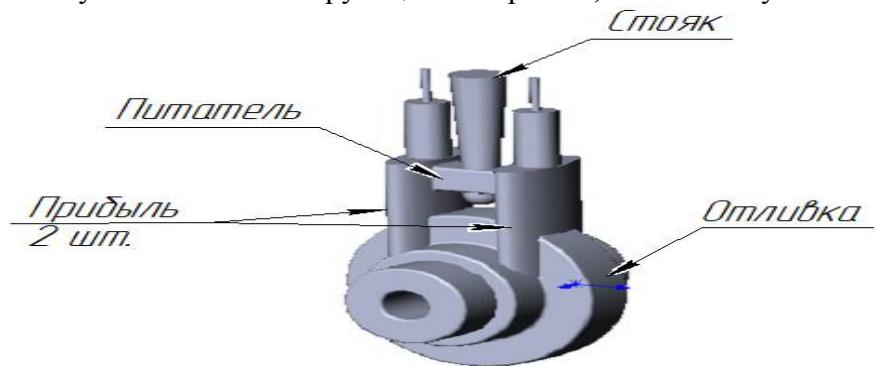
Объемное изображение отливки с верхним подводом металла через прибыль
